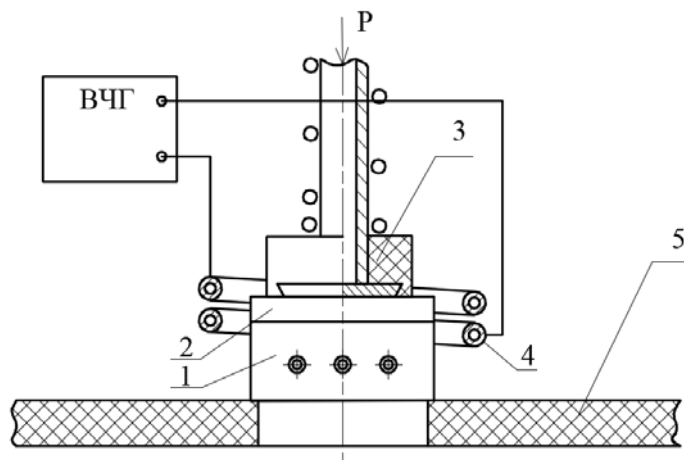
Схема ВЧ-пайки корпусов микроблоков
